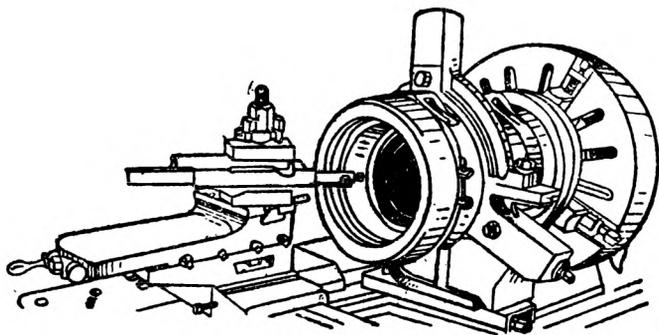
Неподвижный люнет с выточкой для проверки установки кулачков.
